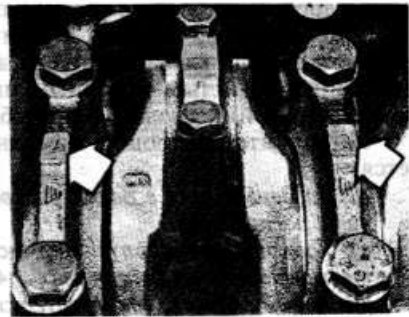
Метки на крышке коренного подшипника (указаны стрелками) — двигатель 1,6 л
